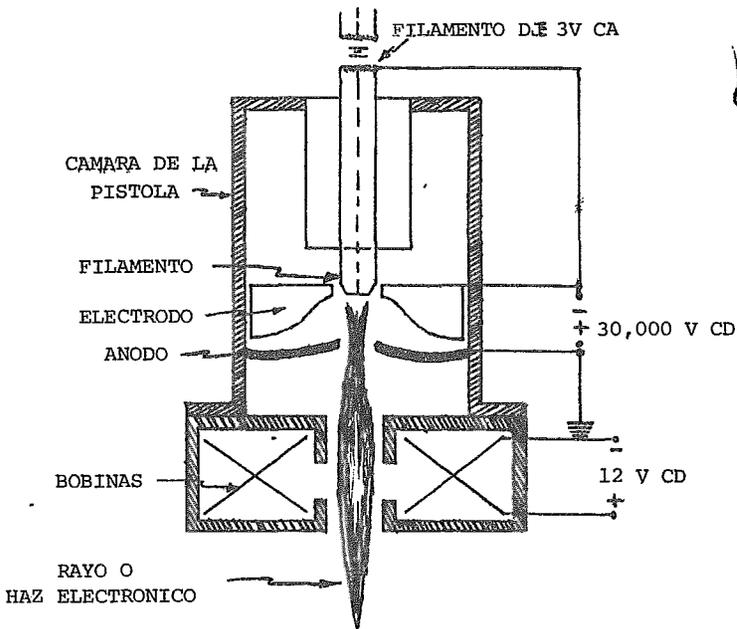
DIAGRAMA ESQUEMATICO DE LA PISTOLA DE ELECTRONES USADA PARA LA SOLDADURA DE HAZ ELECTRONICO
